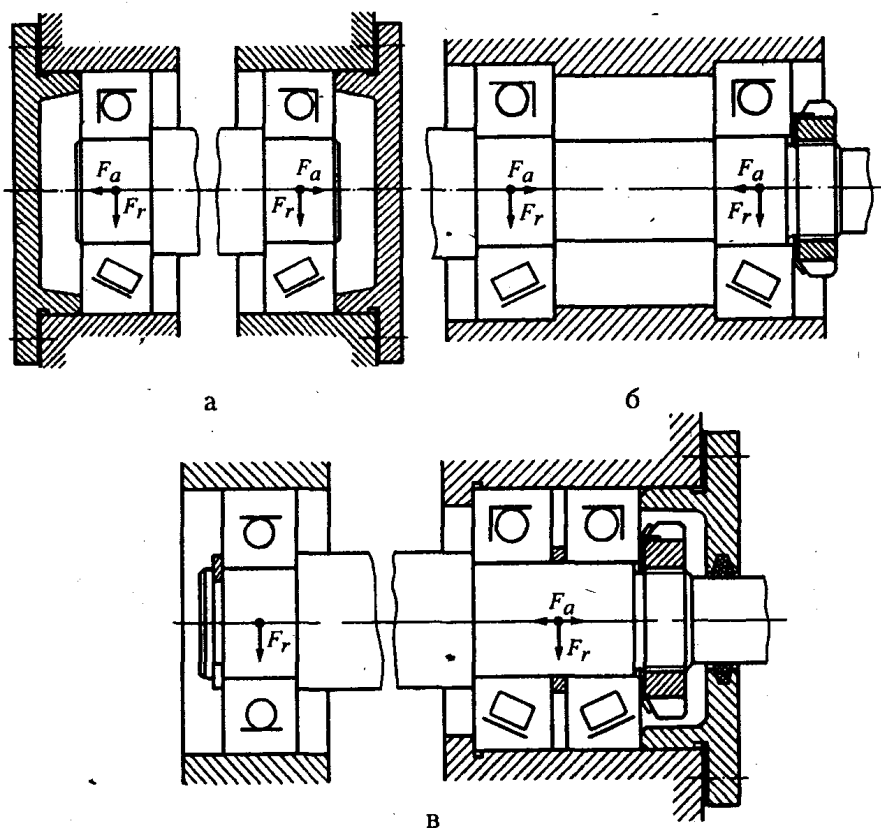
Конструкції опор валів на радіально-упорних підшипниках
